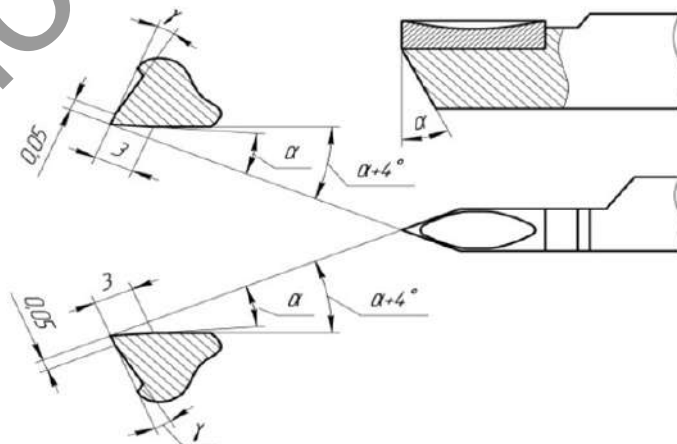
Резьбовой резец со сменной твердосплавной пластиной T14K8 для обработки труднообрабатываемых материалов
